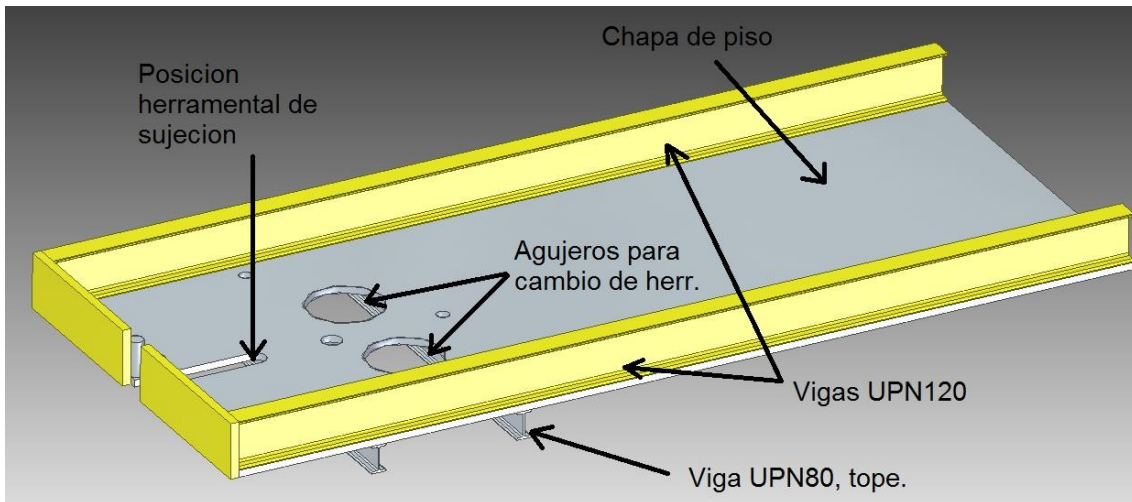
Estructura metálica soporte: Vigas y chapa de piso.
